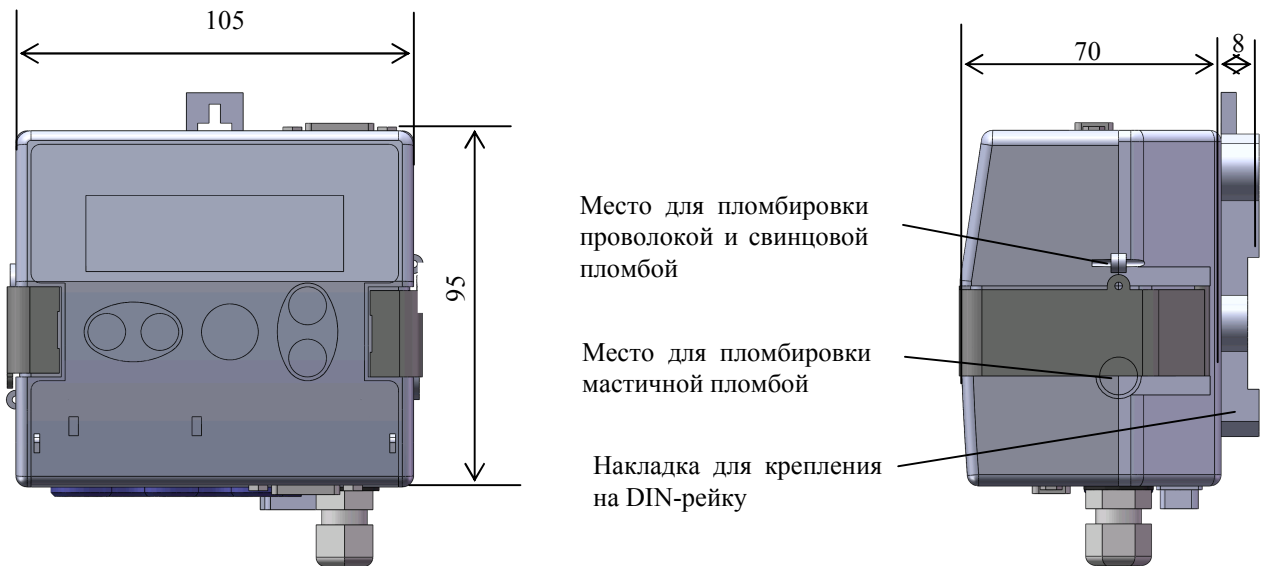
и - Габаритные размеры электронного блока с накладкой для крепления на DIN – рейку
